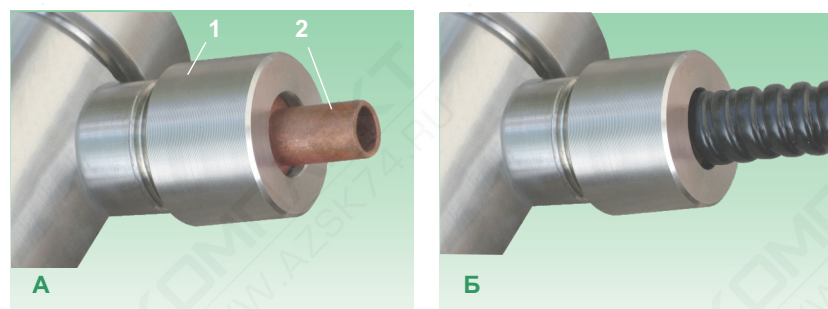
Устройство крепления бронированного кабеля УКБК-15 для кабельного ввода "D12": А - детали устройства (1 - резьбовая конусная втулка, 2 - конусная втулка, 3 - резьбовая втулка); Б - вид в сборе с кабелем.
